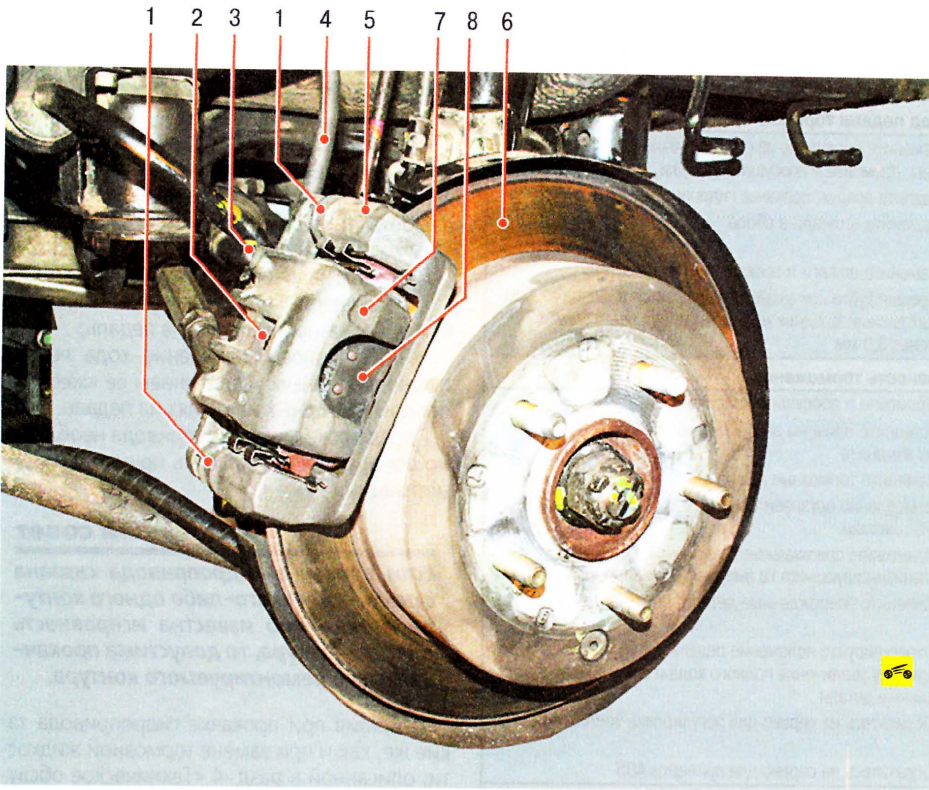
Рабочий тормозной механизм заднего колеса: 1 – направляющие пальцы суппорта; 2 – внутренняя тормозная колодка; 3 – клапан выпуска воздуха; 4 – тормозной шланг; 5 – направляющая колодок; 6 – тормозной диск; 7 – суппорт тормозного механизма; 8 – наружная тормозная колодка
